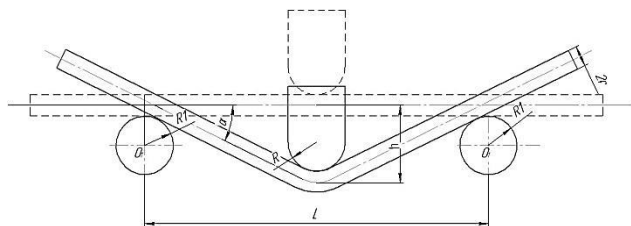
Схема двухопорной гибки заготовки круглого сечения
